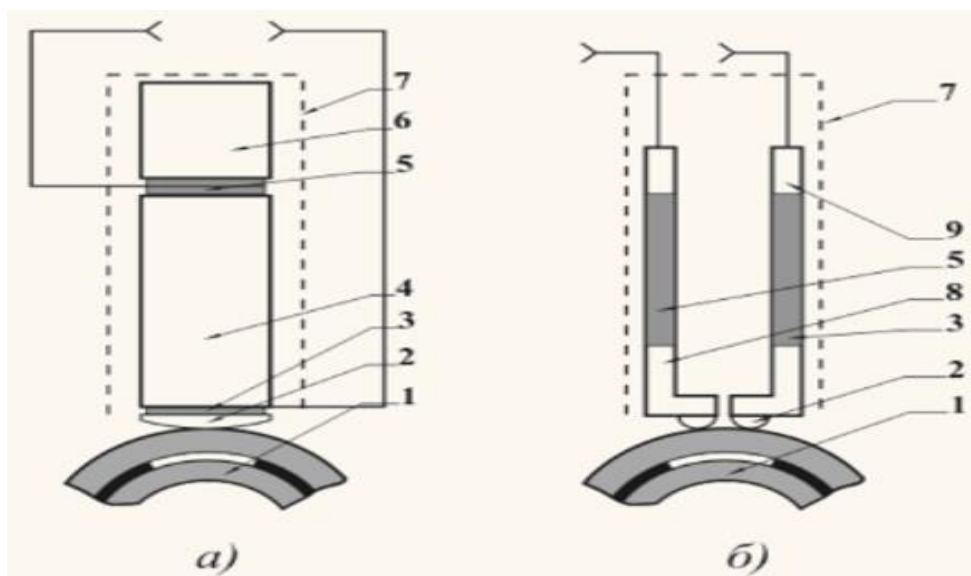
преобразователи импедансного дефектоскопа: 1 - контролируемый объект; 2 - контактный наконечник пьезоэлементов; 6 - тыльная масса; 7 - корпус преобразователя; 8 - излучающий вибратор; 9 - приемный вибратор.
